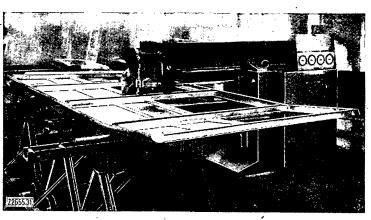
Schweißen von Leichtmetall-Seitenwänden für Eisenbahnwagen auf einer Hochleistungs-Punktschweißmaschine.
